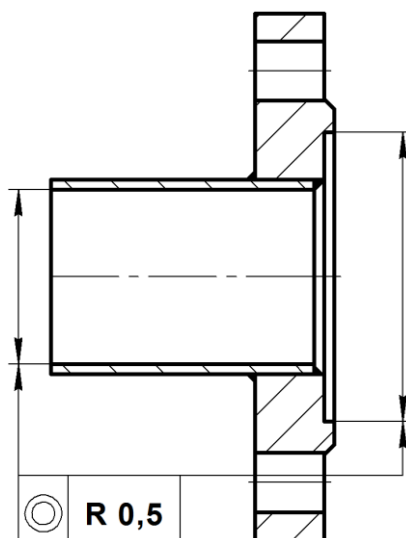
Схема взаимного расположения трубопровода и фланца при приварке (Ду 65 и менее)
